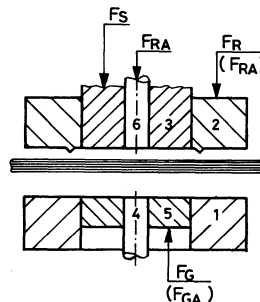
Bezeichnung der Kräfte im Feinschneidwerkzeug
